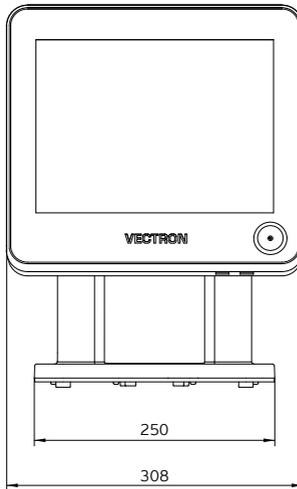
POS Touch 12 Dimensions pied S420 inclu (en mm)
